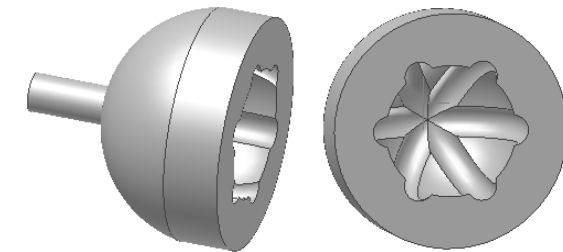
Общий вид модели корпуса сферического шарнира
